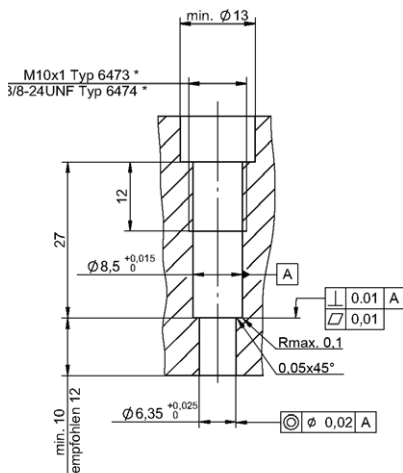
Bohrung für Direkteinbau mit Montagenippel
